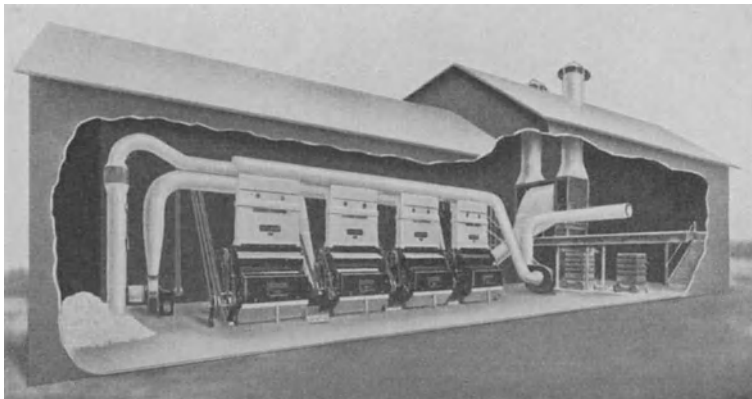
Vier Säge-Egreniermaschinen mit je 80 Sägen und pneumatischer Fasergutförderung nach Patent Murray (Platt Brothers & Co. Ltd., Oldham).
